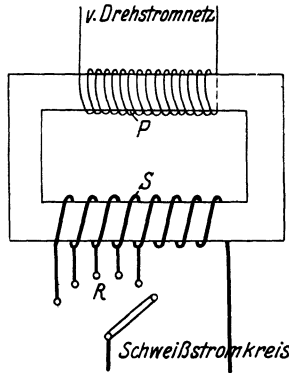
Schweißumspanner mit Anzapfregelung.
